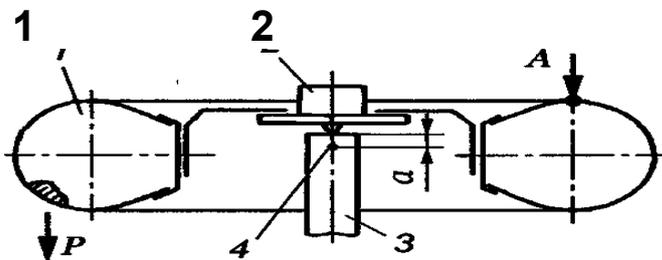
Статическая балансировка колеса: a — расстояние от центра тяжести колеса до опорной поверхности; 1 — колесо; 2 — приспособление; 3 — опора; 4 — центр тяжести колеса.
